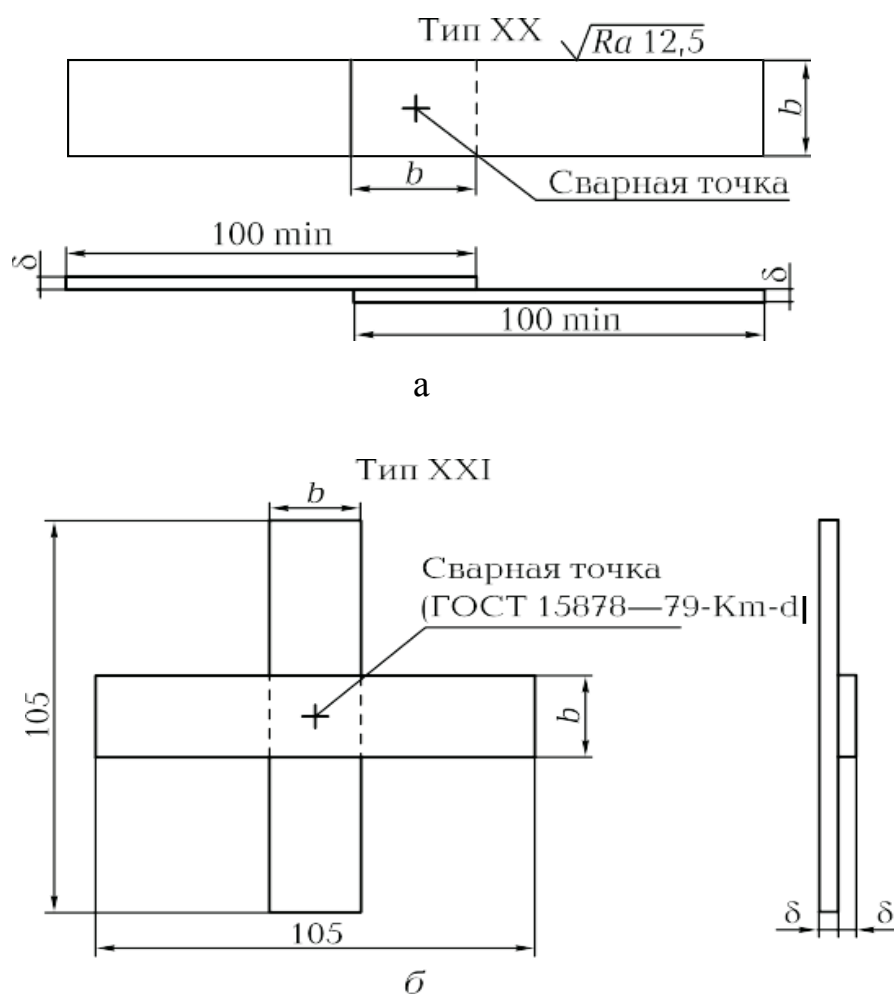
Образцы для механических испытаний контактной точечной сварки [2]:
